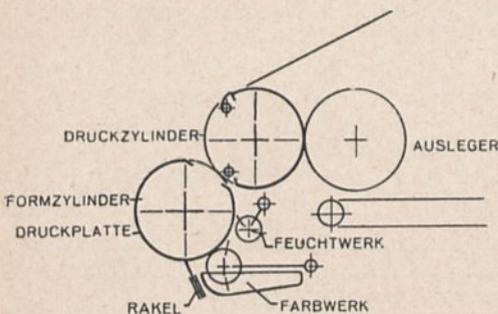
Schema einer Schwartzkopff-Plattentiefdruckmaschine mit gleich großem Druck- und Formzylinder in schräger Anordnung
